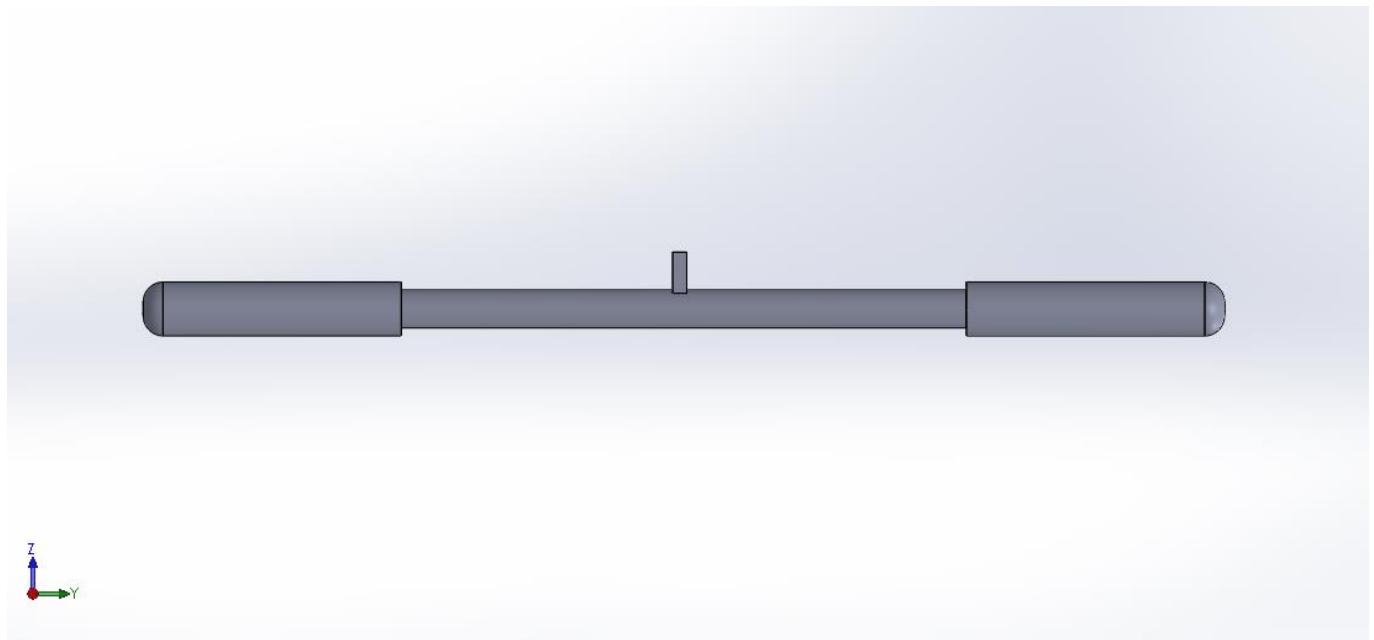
Δημιουργία δεύτερου εξωτερικού περιβλήματος με την χρήση εντολής MIRROR
